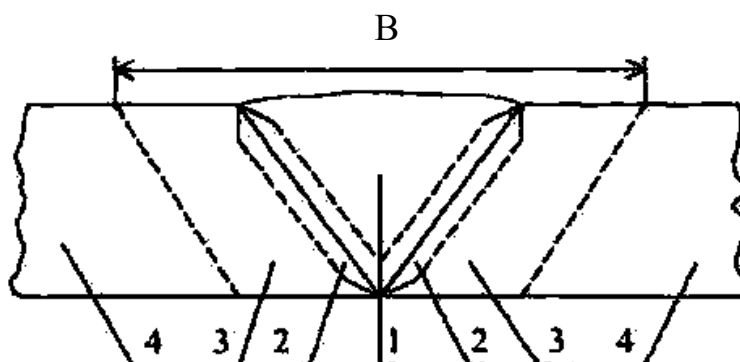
Схема будови зварного з'єднання: 1 – зварний шов; 2 – ділянка неповного розплавлення металу; 3 – зона термічного впливу; 4 – основний метал; В – загальна величина зони термічного впливу
